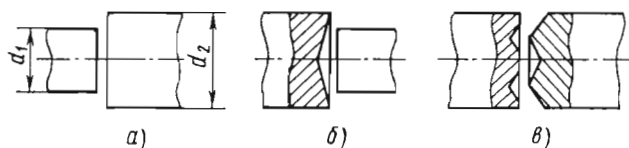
Подготовка контактных поверхностей заготовок из разнородных материалов к сварке: а – из быстрорежущей стали и конструкционной; б – из коррозионно-стойкой стали и алюминия; в – из коррозионно-стойкой стали и цинка;  $d_2 = (1,15 \dots 1,25)d_1$
